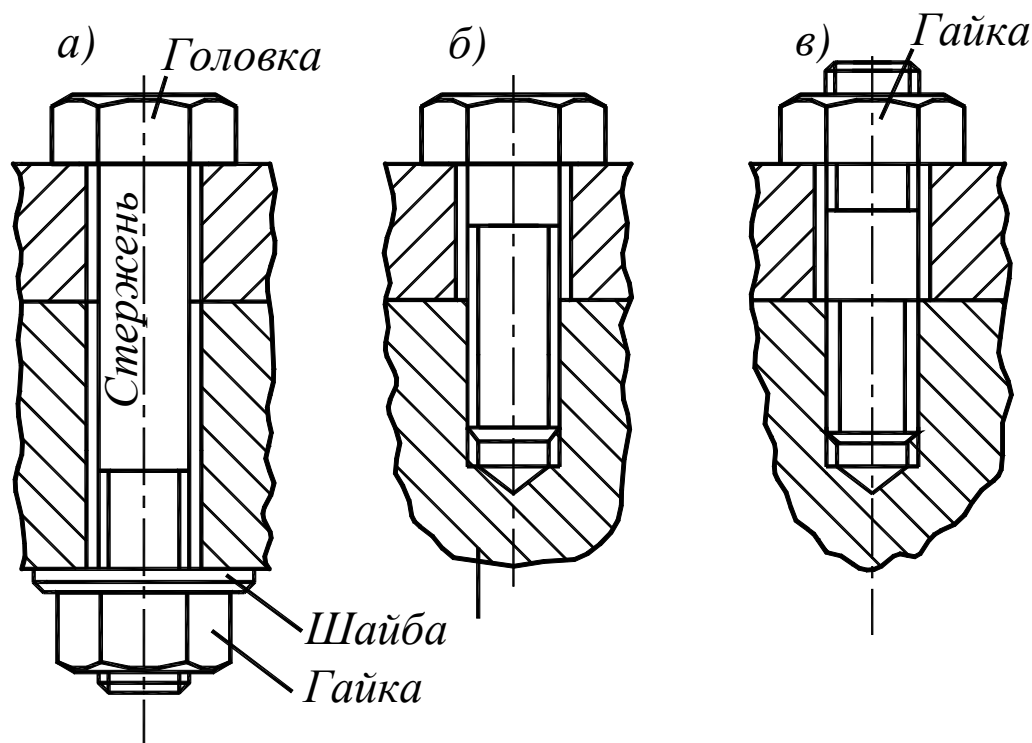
Виды резьбовых соединений: а) болтовое; б) винтовое; в) шпилечное
